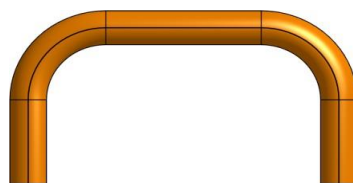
Tubos que são confeccionados em máquina de dobra CNC, para condensador de ar condicionado.
